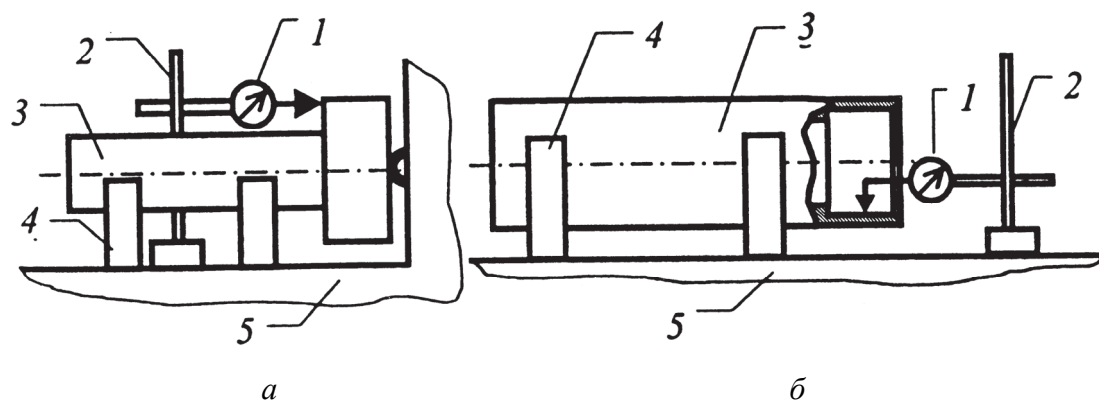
Схемы приспособлений для контроля точности расположения поверхностей
